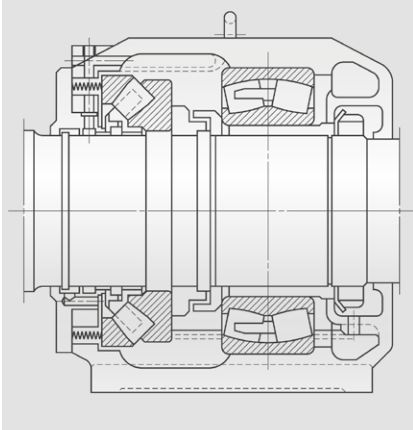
Установка преднатяга упорных роликоподшипников (с помощью пружины)
